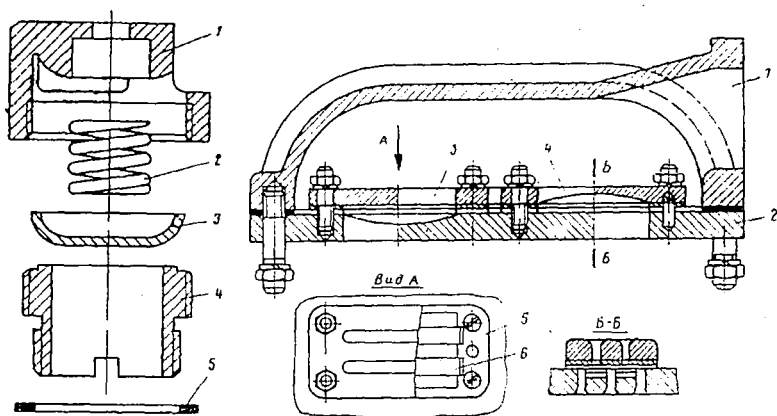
Тарельчатый воздухораспределительный клапан компрессора ЗИС
